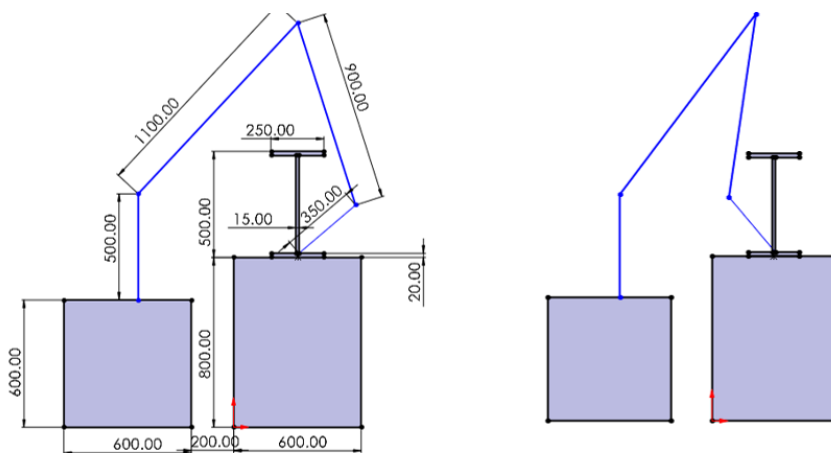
Dimensionamiento del sistema de soldadura
